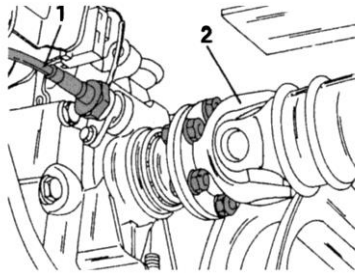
Розташування приводу тахометра на коробці передач:
